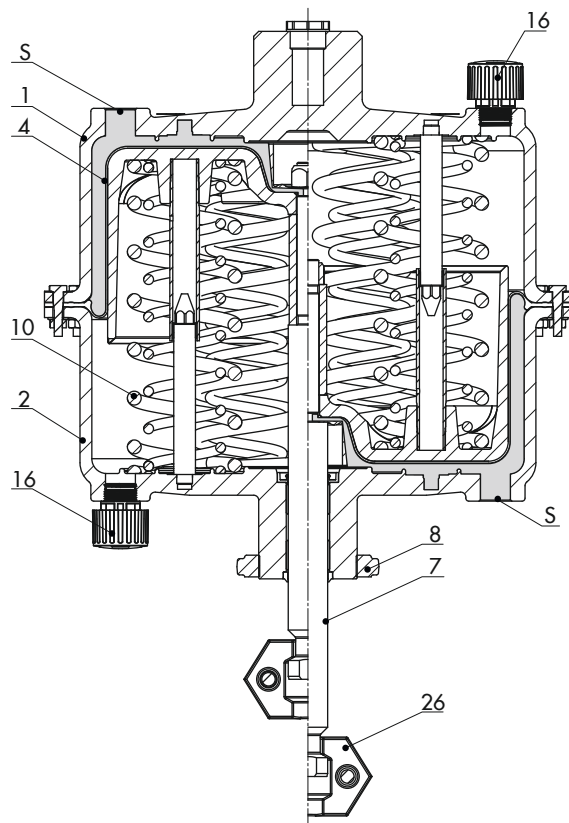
Typ 3271, Ausführung 1400-120 cm² mit Innengewinde am oberen Deckel
